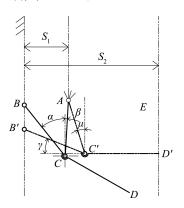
开袋机构参数设计 Fig.8 Parameter design of bag opening mechanism
